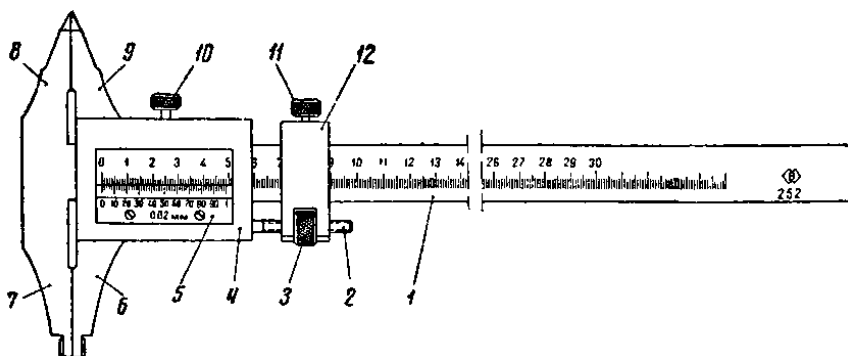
Конструкция штангенциркуля ШЦ-II: 1 – штанга; 2 – винт микрометрической подачи рамки; 3 – гайка микровинта; 4 – рамка; 5 – нониусная пластинка; 6 и 9 – подвижные губки; 7 и 8 – неподвижные губки; 10 и 11 – стопорные винты; 12 – хомут;
